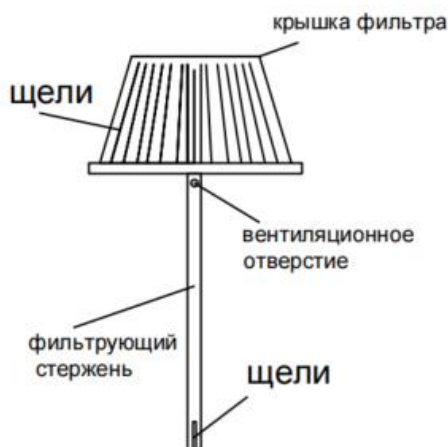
Конструкция фильтрующей головки с длинной ручкой
